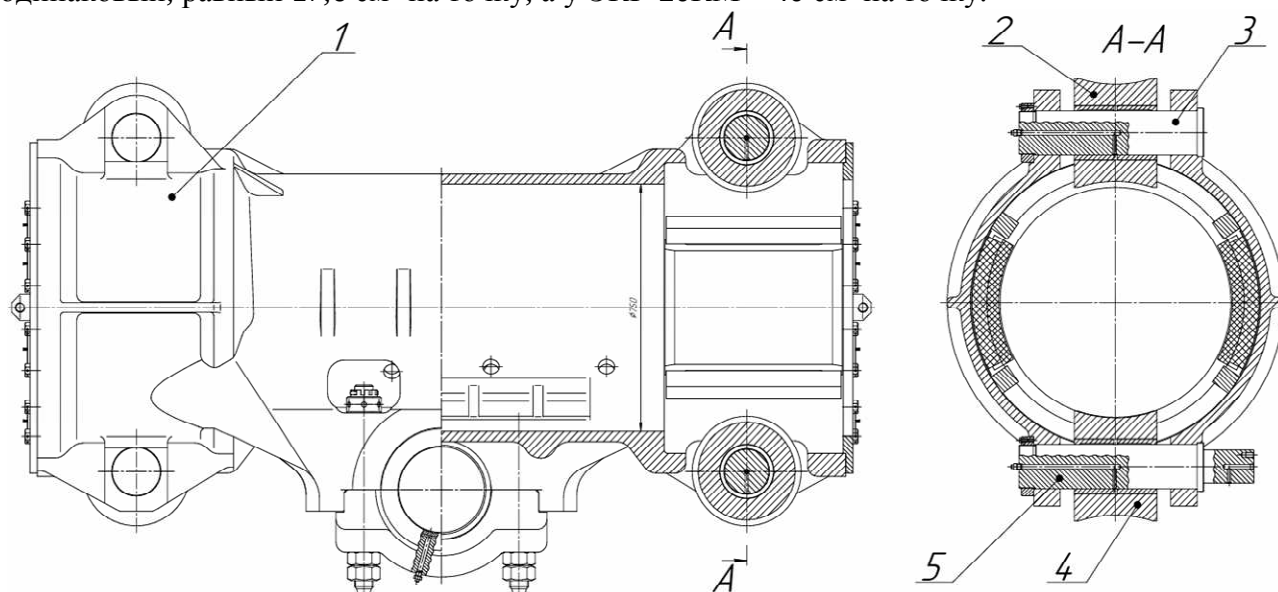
Конструктивная схема седлового подшипника экскаватора с канатным исполнением напорного механизма (материалы автора): 1 – седловой подшипник, 2 – ролик верхний, 3 – ось ролика верхнего, 4 – ролик нижний, 5 – ось ролика нижнего
